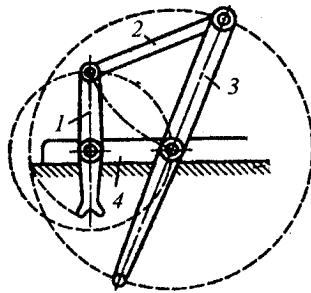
Механізм нерівномірного руху (шарнірний чотириланковик) з приспособленням для переходу через мертву точку
